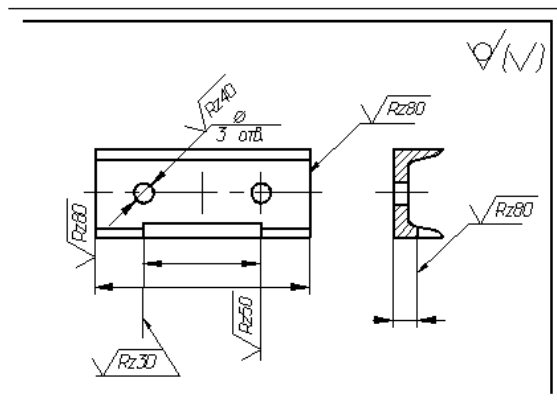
Указание шероховатости, когда большая часть поверхностей не обрабатывается по данному чертежу
